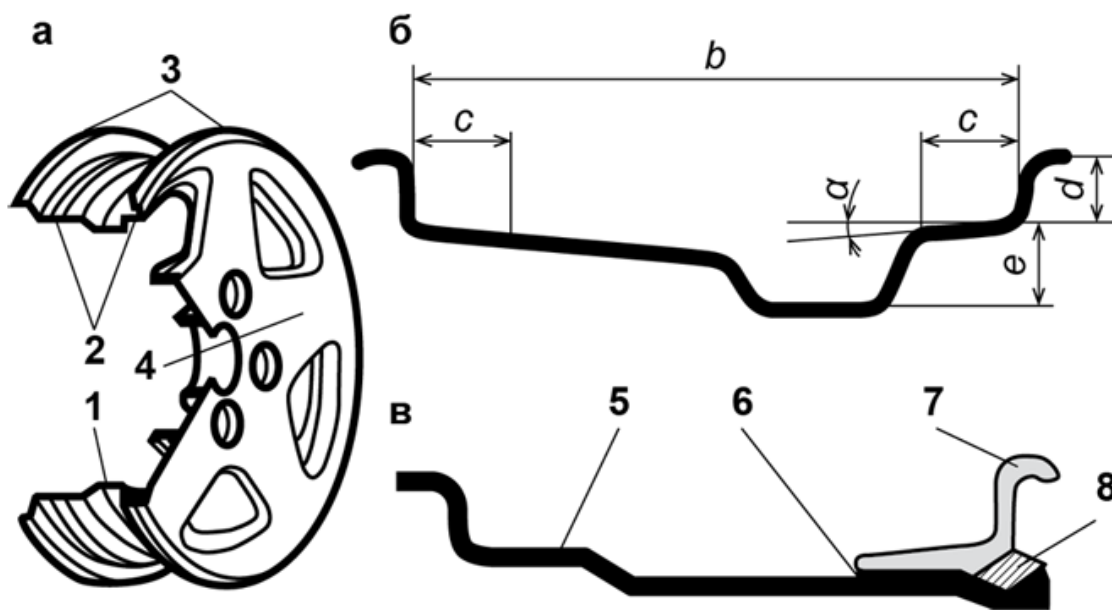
Автомобильный колесный диск: а – основные элементы конструкции диска; б – основные элементы неразборного обода; в – разборный трехкомпонентный обод; 1 – центральная цилиндрическая часть обода; 2 – полки обода; 3 – фланцы (закраины обода); 4 – диск колеса; 5 – цилиндрическая часть; 6 – резиновое кольцо; 7 – съемный фланец; 8 – пружинное запорное кольцо; α – угол наклона полки обода
